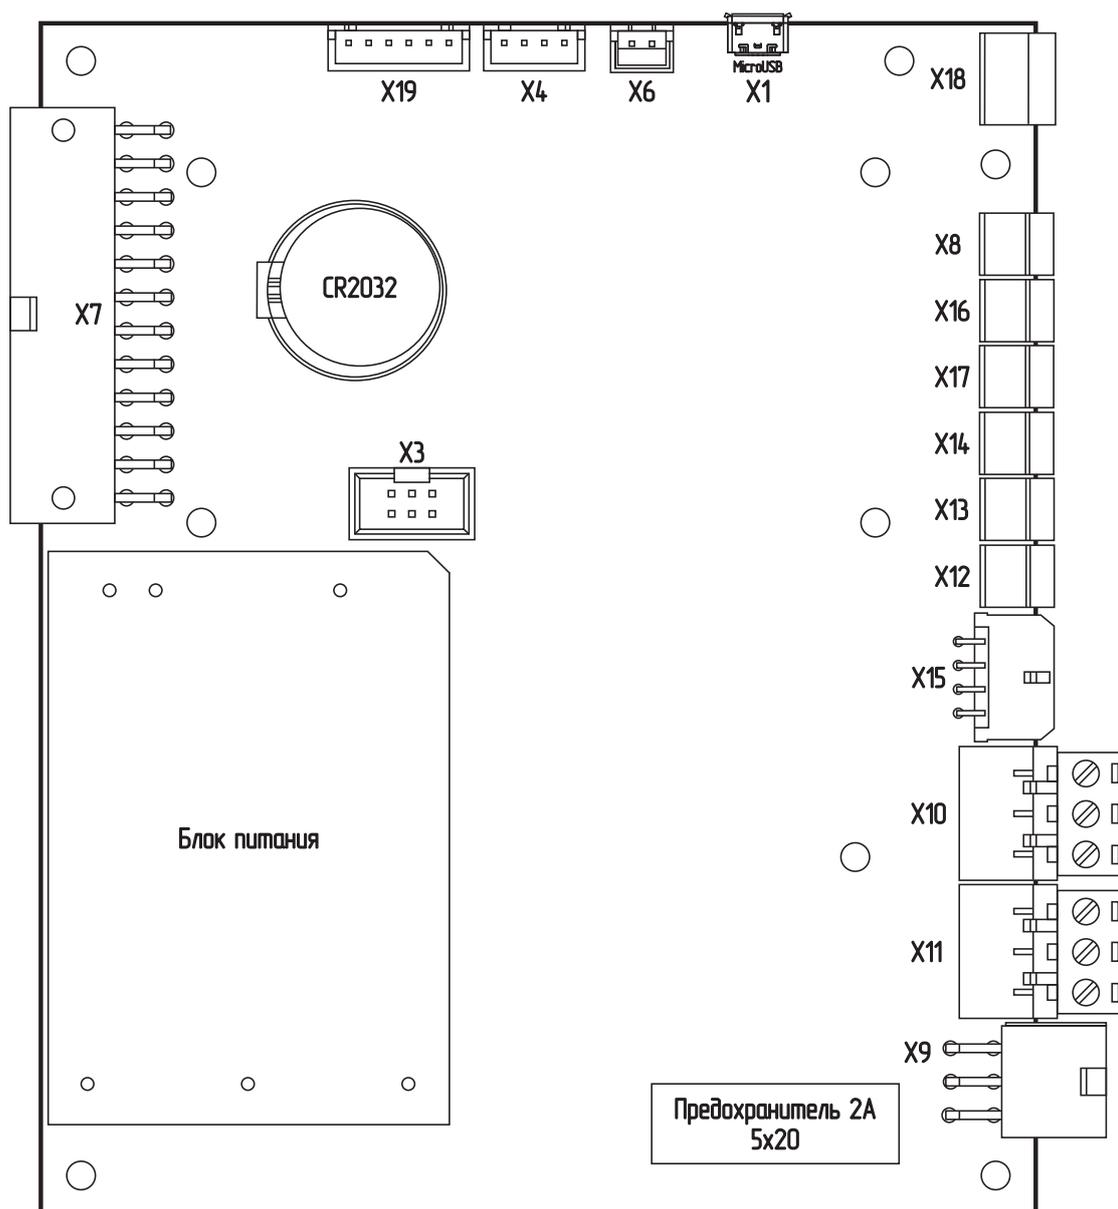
Корпус контроллера «ZOTA X-Line 100E»
